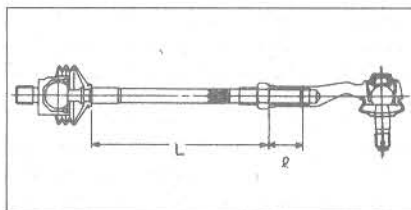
Основные установочные величины рулевой тяги (Глава 36)
